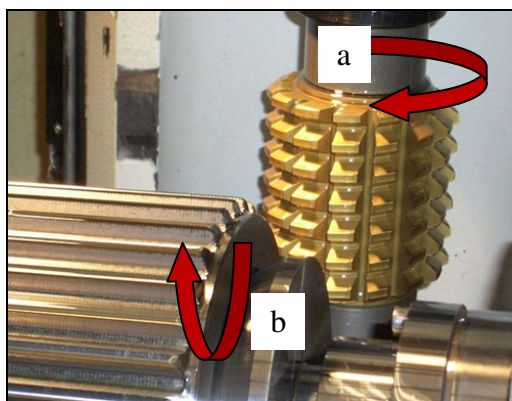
Foto de geração de engrenagens por cortador Caracol
